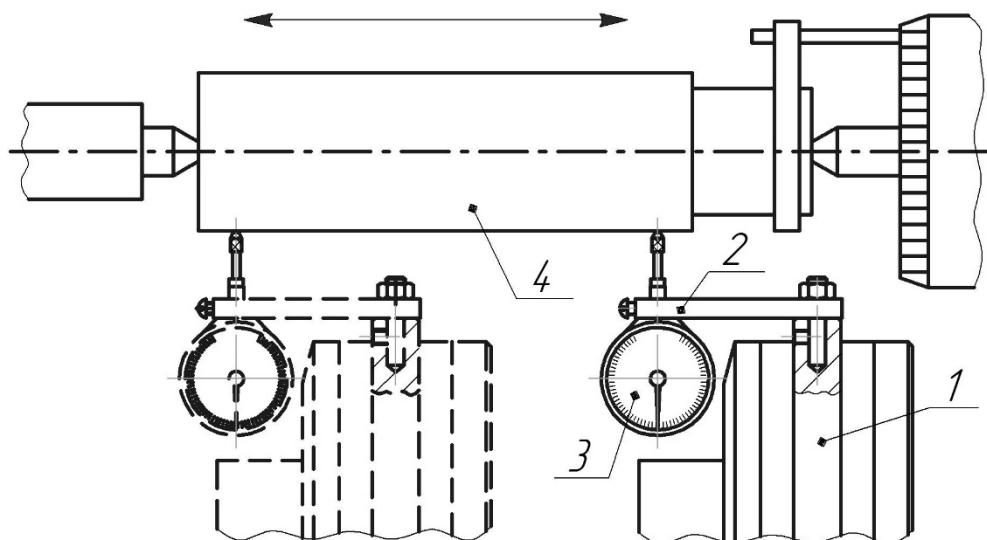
Схема контроля и корректировки положения вала-образца
